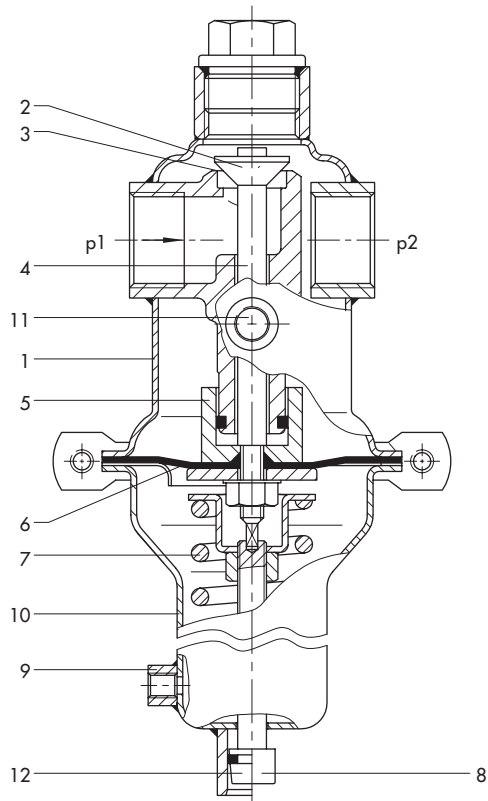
· Редуктор тип М 44-2 (ряд 0,02 до 12 бар)
